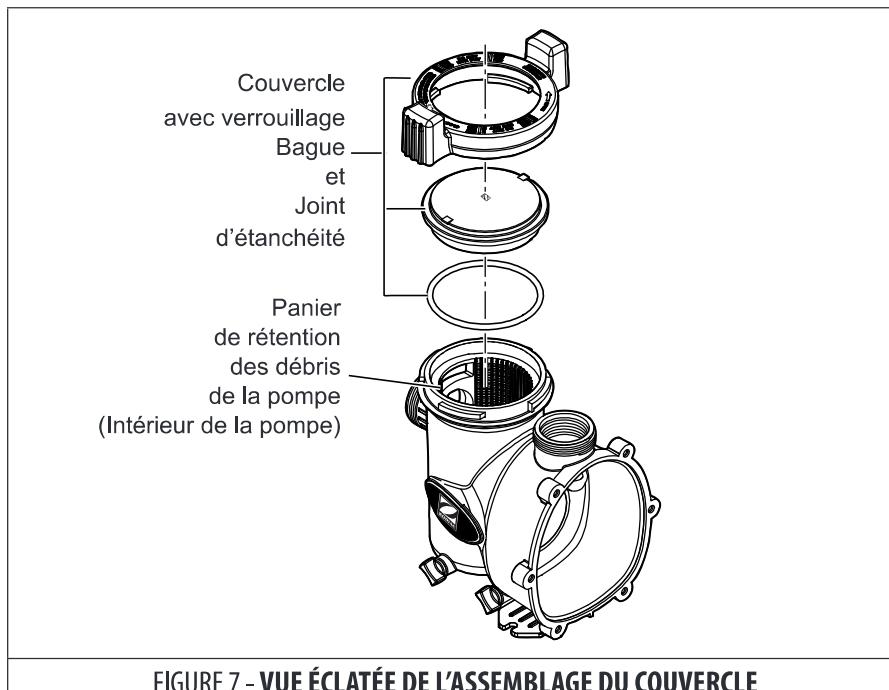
VUE ÉCLATÉE DE L'ASSEMBLAGE DU COUVERCLE
